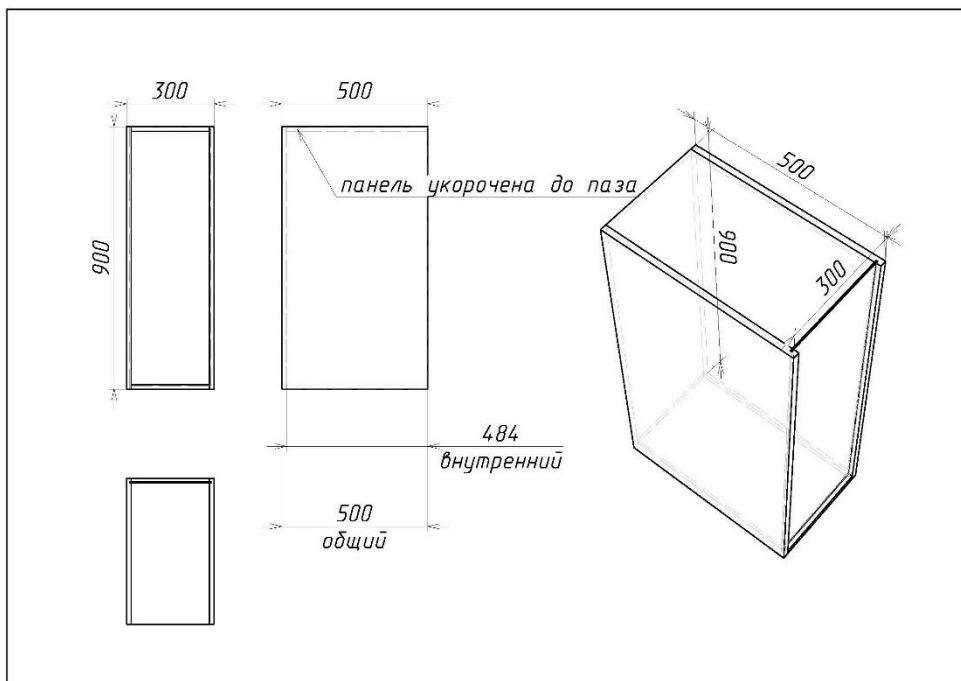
Установка задней стенки в паз в корпус с вкладными крышкой и дном (БМ)
